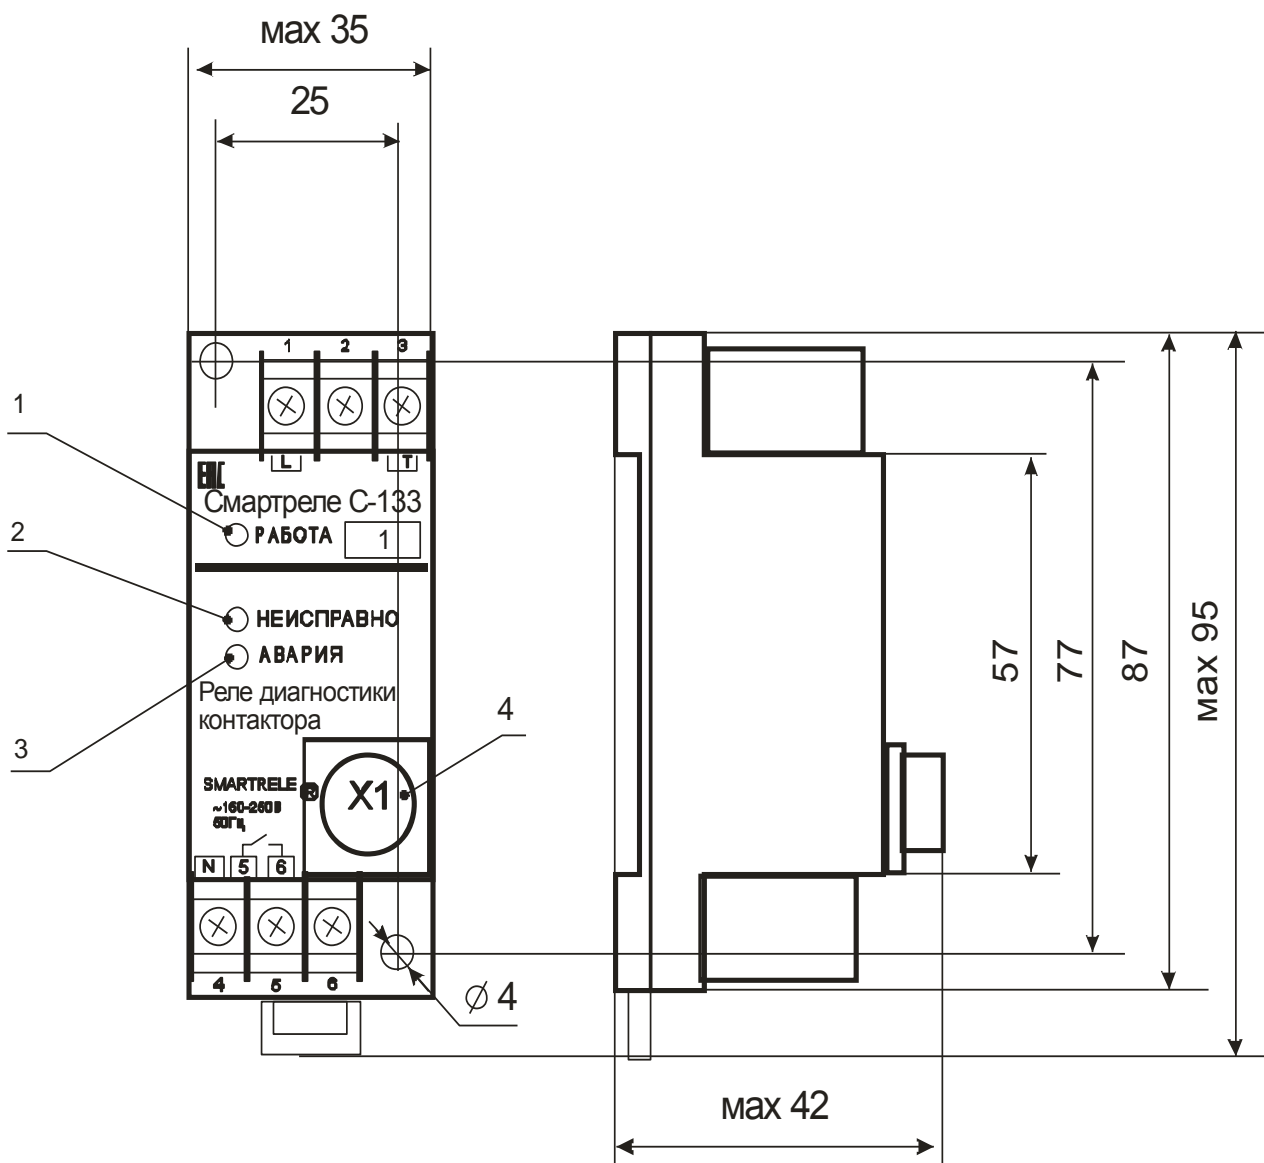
внешний вид, габаритные и установочные размеры СМАРТРЕЛЕ С-133
